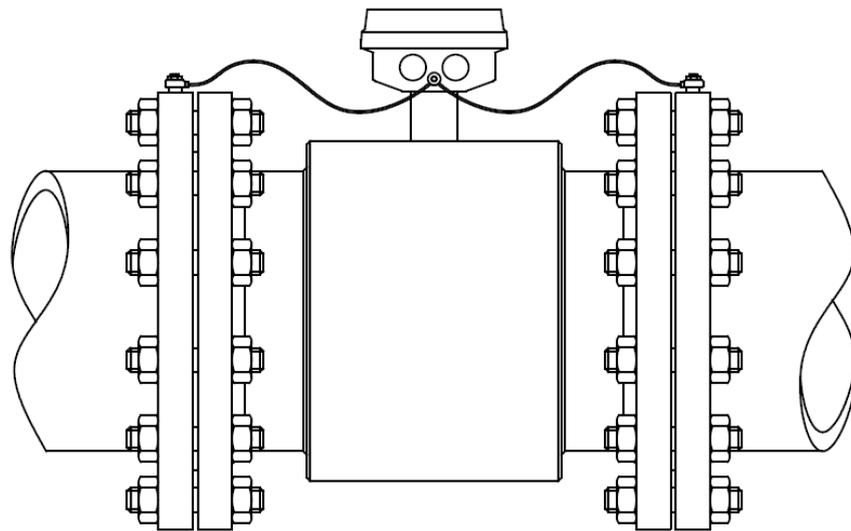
Medidor Flangeado, aterrado em tubulação condutiva com flanges soldados
